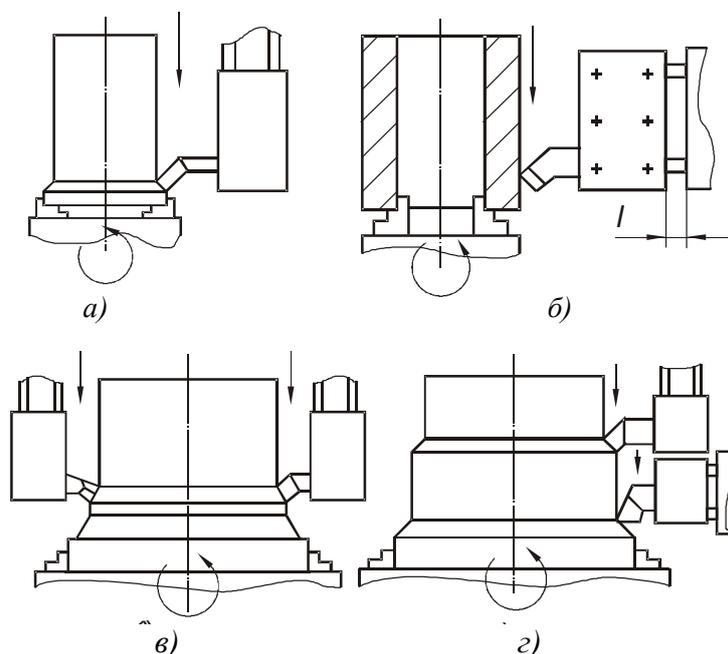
Схемы обработки на токарно-карусельных станках
